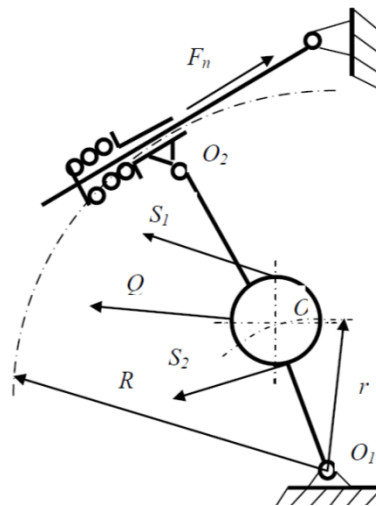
Розрахункова схема для визначення необхідного зусилля пружини
